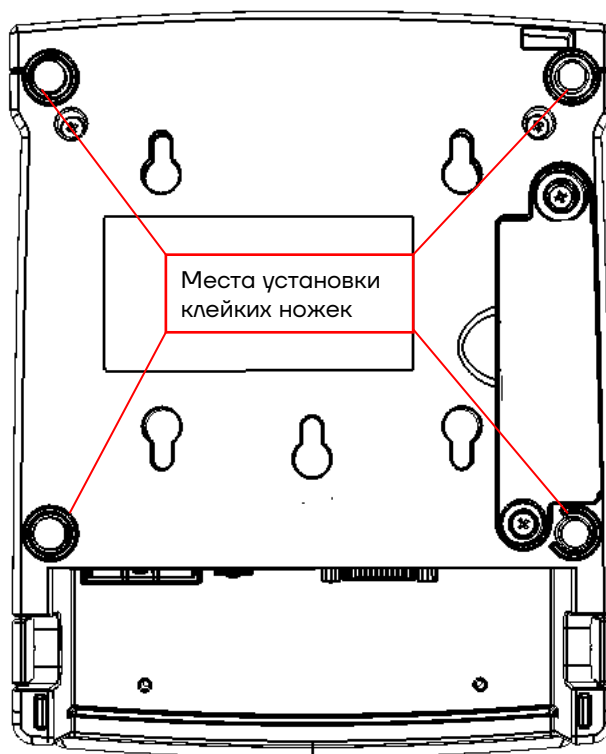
Места установка клейких ножек на дне корпуса изделия
